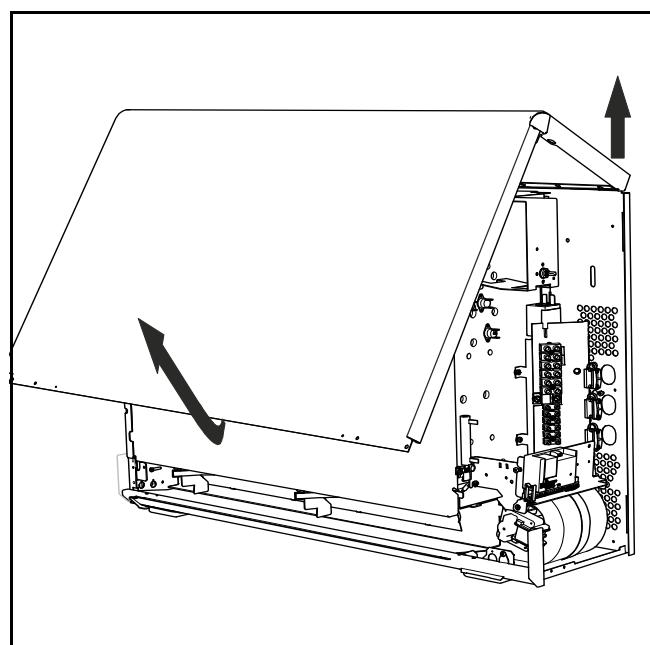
Piovez la paroi avant vers l'avant tout en la soulevant légèrement et sortez-la de la fixation arrière.
